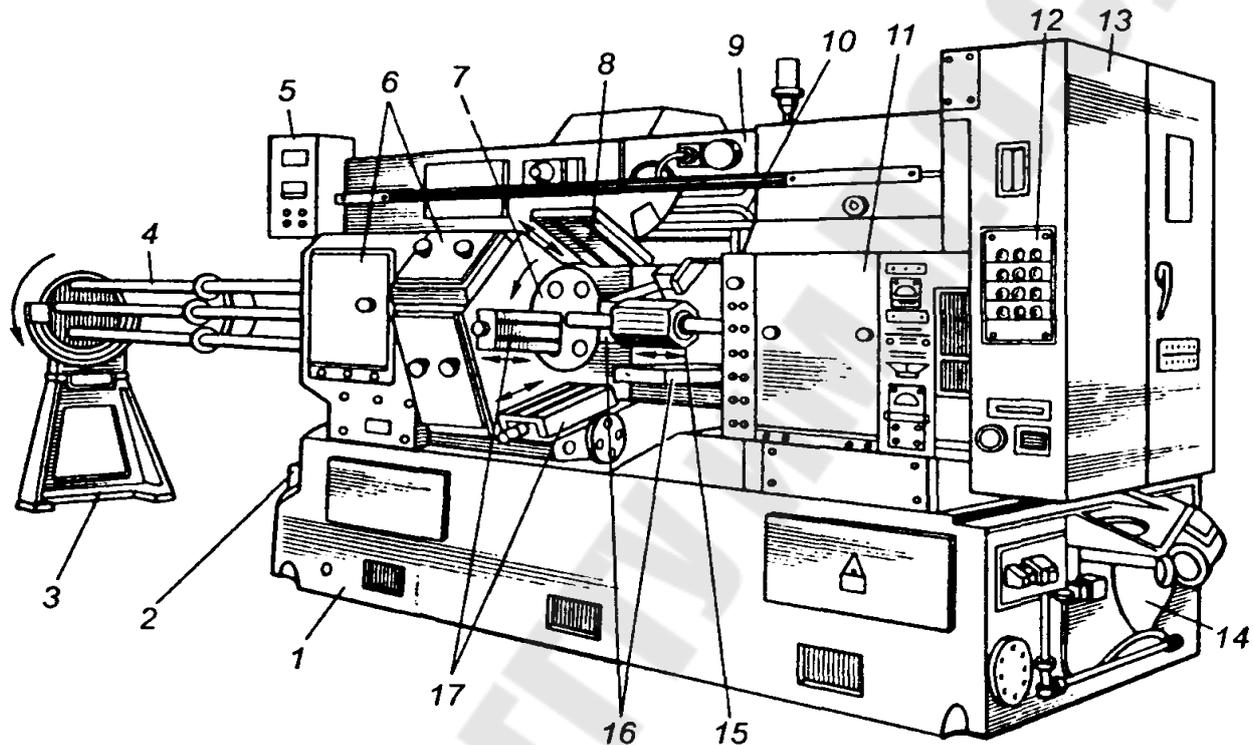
Общий вид токарно-револьверного шестишпindelного автомата
